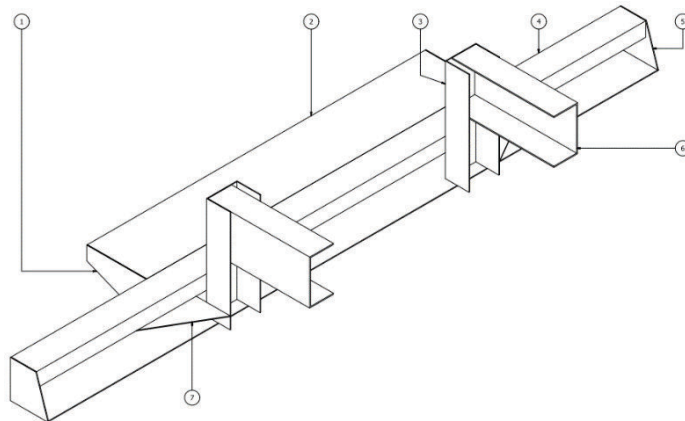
Dispositivos antiempotramiento de plancha corrugada tipo grada.
